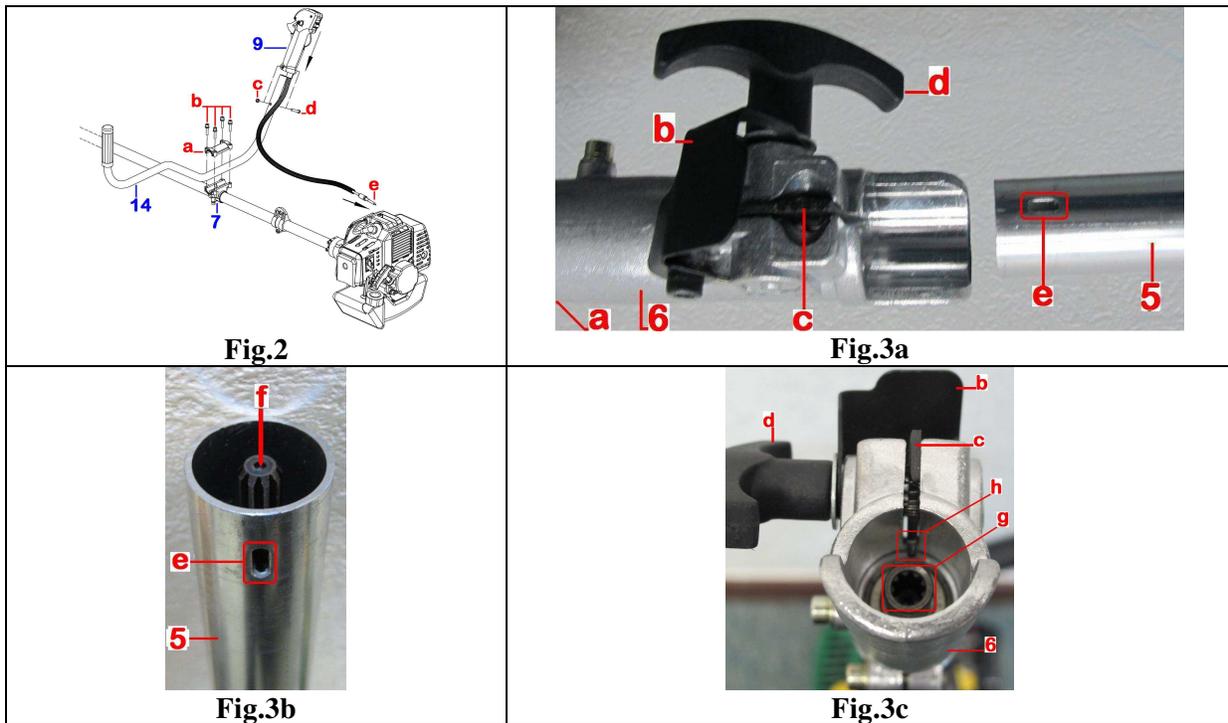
a- Tube coté moteur ; b- Plaque de blocage ergot ; c- Déverrouillage ergot de sécurité ; d- poignée ; e- encoche d'accroche ergot de sécurité ; f- arbre entrainement tube accessoire ; g- arbre d'entrainement moteur ; h- ergot de sécurité ; 5- tube accessoire ; 6- connecteur.
